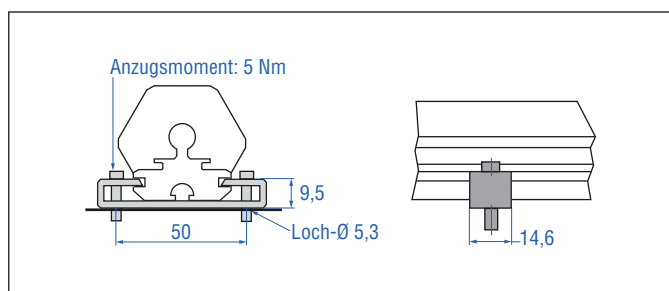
Montageklammern (Artikelnr. 400 802) mit Zylinderschraube M5×20
